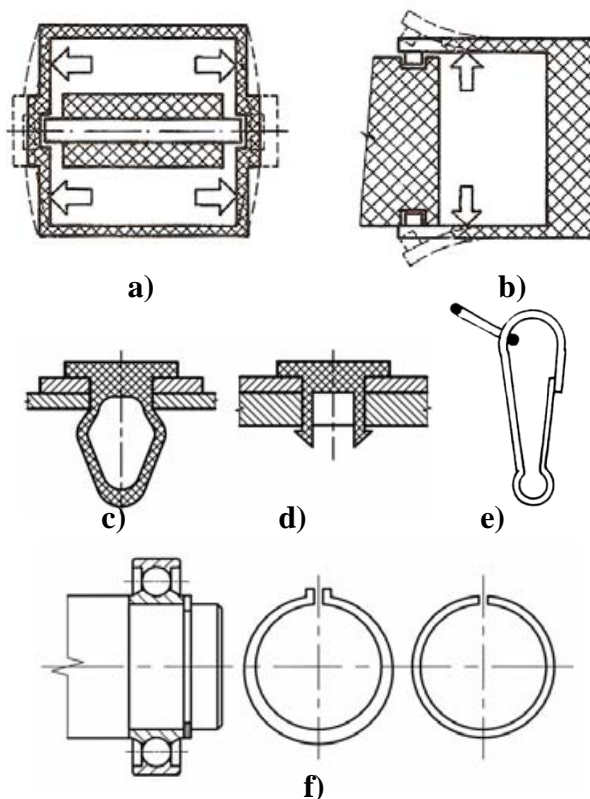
Spoj pomocou príchytky (hmoždinky) [130].
